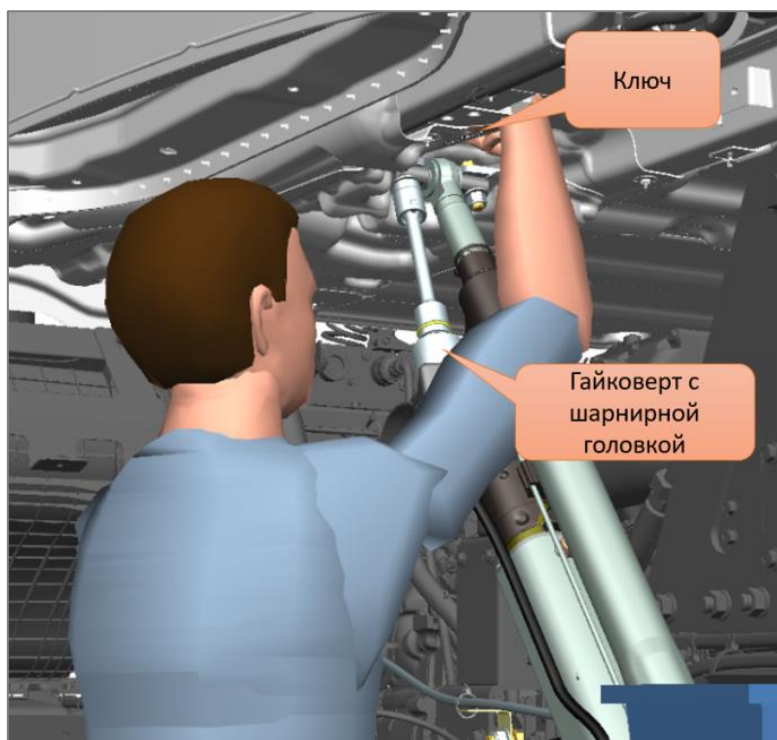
Процесс затяжки гидроцилиндра ключом и гайковертом с шарнирной головкой
